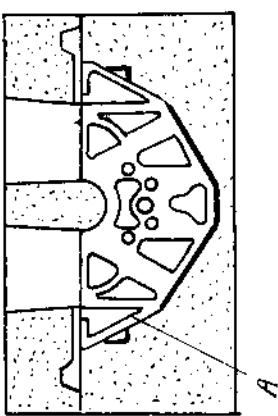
Схема формовки верхнего картера фланцем вниз, подвод металла снизу.
